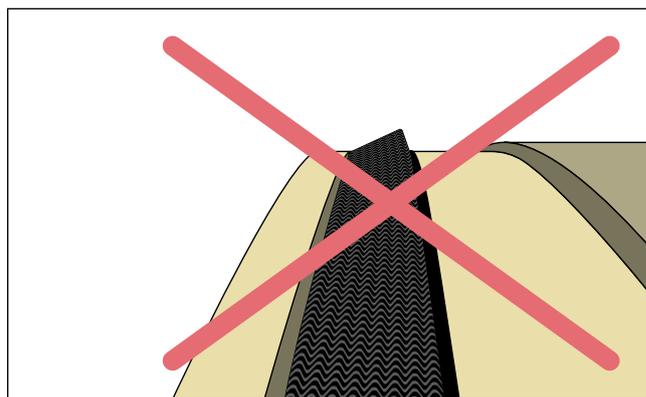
Posicionamento incorreto da junta no interior da ranhura (junta virada ao contrário)
